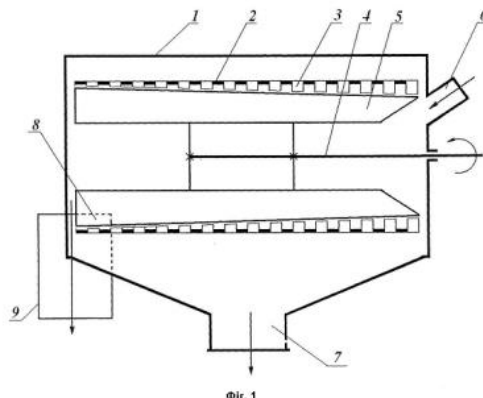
Конструктивна схема протиральної машини: 1 – корпус; 2 – барабан із перфорацією; 3 – робоче сито; 4 – вал; 5 – бичі; 6 – патрубок подачі (приймання) сировини; 7 – випускний патрубок; 8 – отвір; 9 – циклон.
